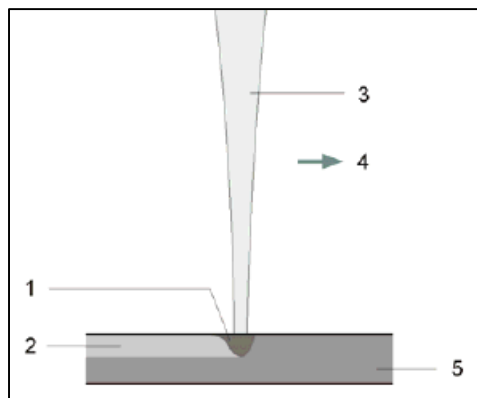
Princípio da soldadura por condução de calor. 1 – material fundido; 2 – cordão de soldadura; 3 – raio *laser*; 4 – sentido da soldadura; 5 – peça de trabalho.
